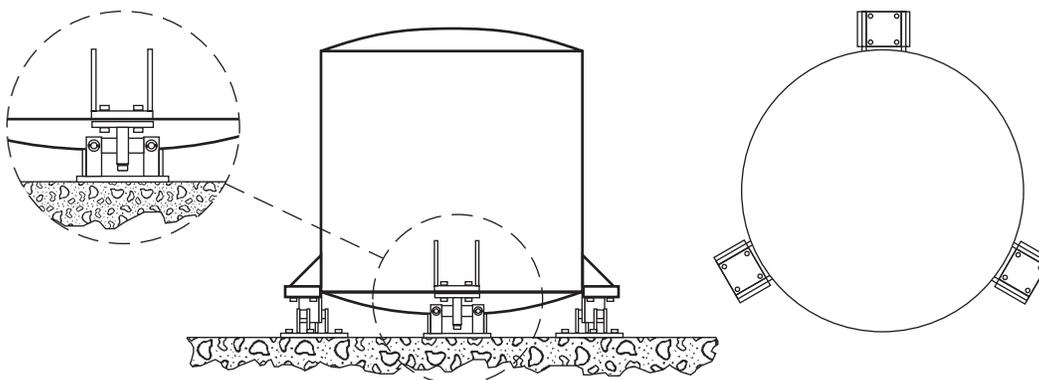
Módulos de pesaje RL1600 en tanque de perfil bajo
